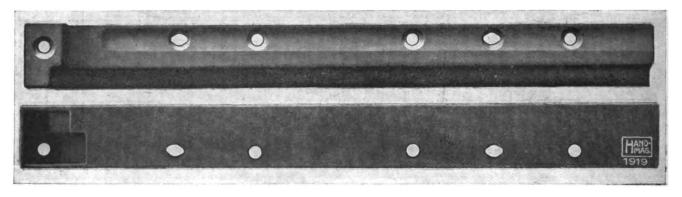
Endplatten-Querschnitt B mit Kopfstück.
